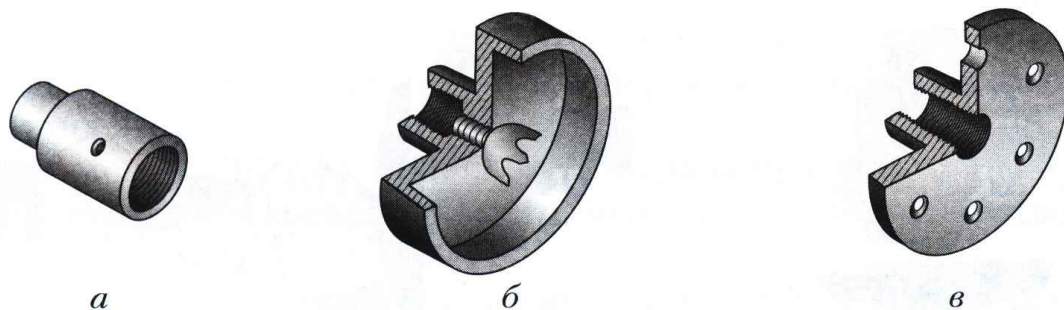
Приспособления для закрепления заготовок: *а* – патрон; *б* – трезубец; *в* – планшайба
